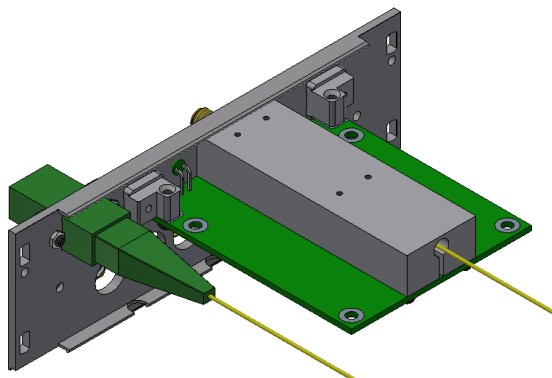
Fissaggio ricevitore ottico su pannello frontale
